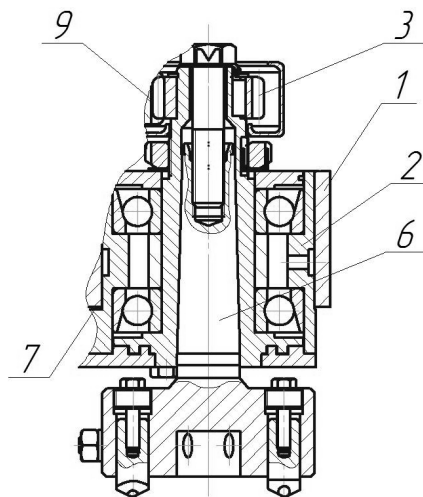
Торцевий багатолезовий інструмент із планетарним рухом формують елементів
